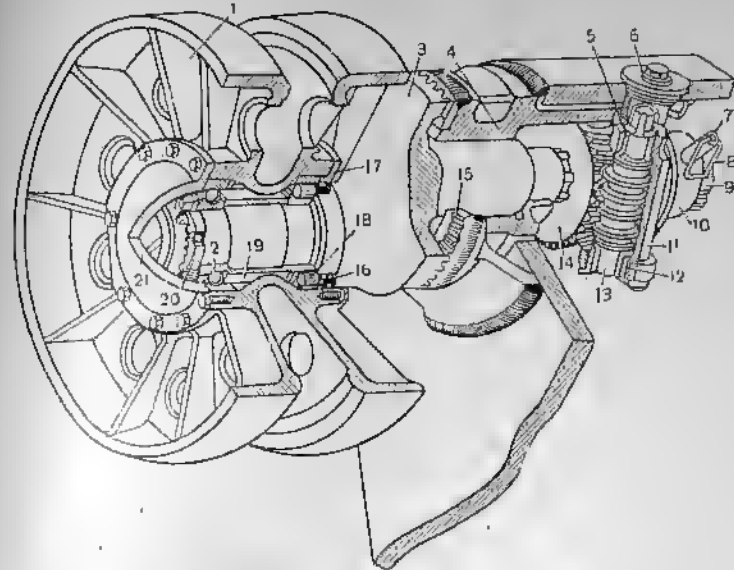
Направляющее колесо (ленивец) и натяжной механизм:
